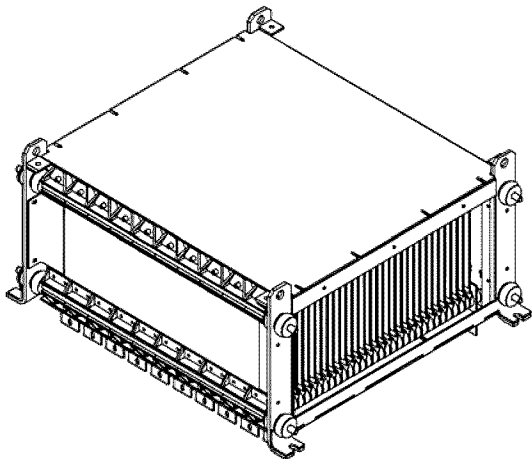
Внешний вид блока тормозных резисторов
